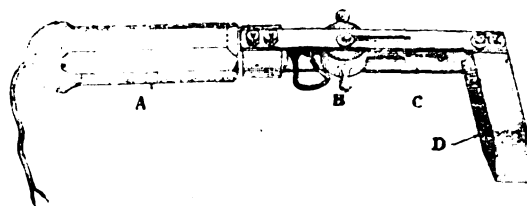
Vue d'un fer à souder, à arc électrique (MM. Coeuille et C<sup>ie</sup>).
